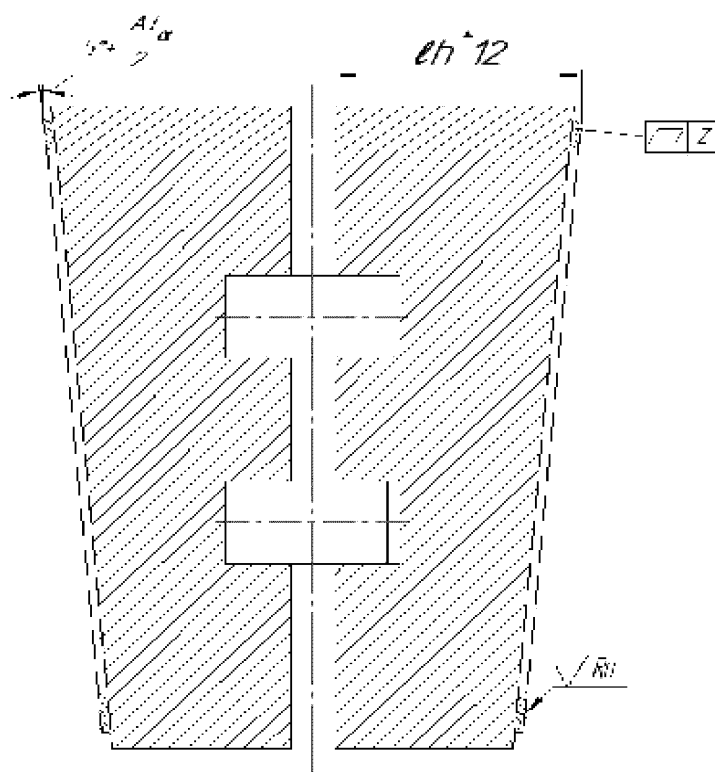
Седло корпуса под упругий и двухдисковый клин
